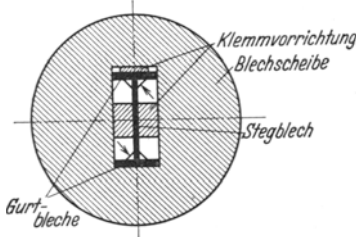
Einspannvorrichtung für das Schweißen von Trägerprofilen.
